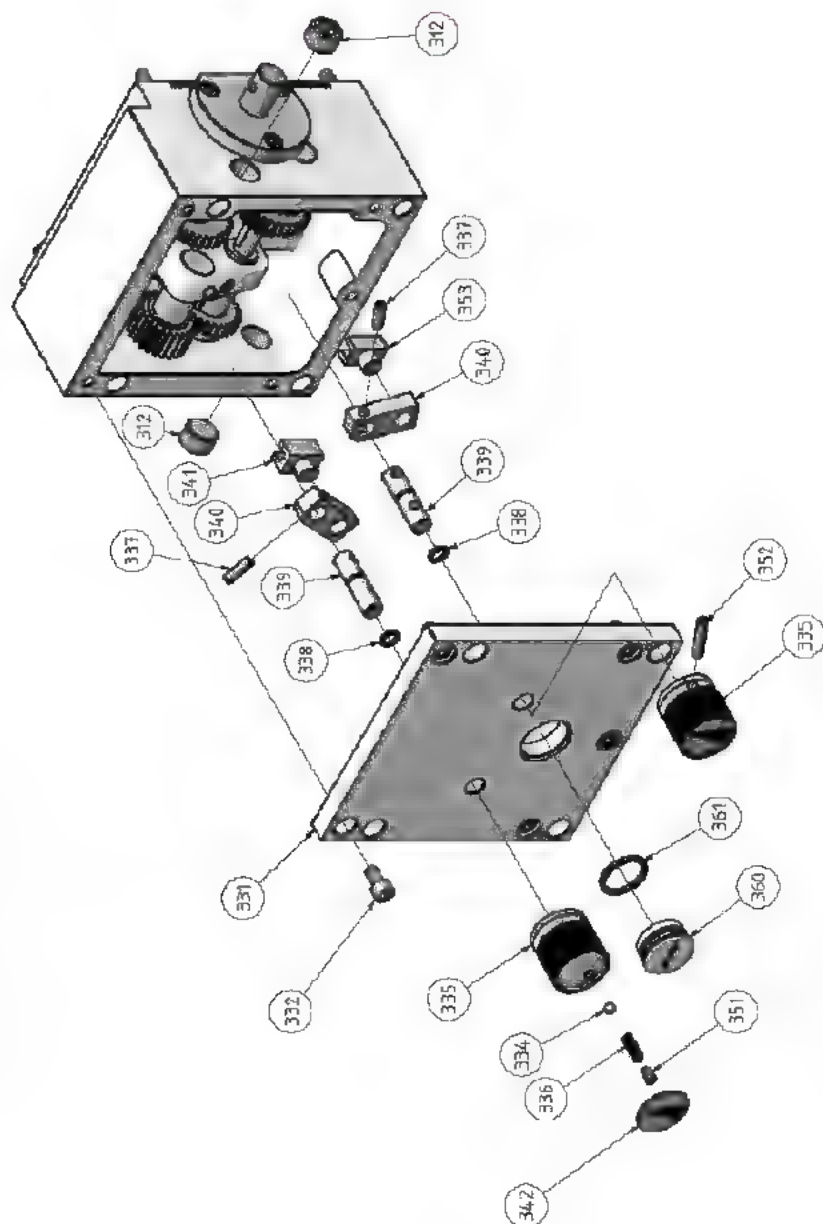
Vorschubgetriebe D240 1 von 2 - Feed gear D240 1 of 2
